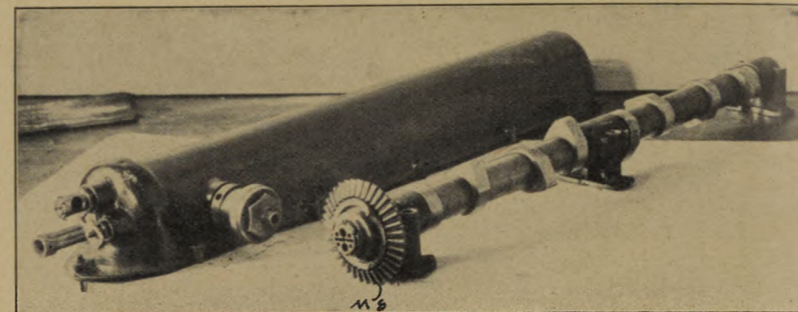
Steuerwelle (MG-Nocken) für das Maschinengewehr.
